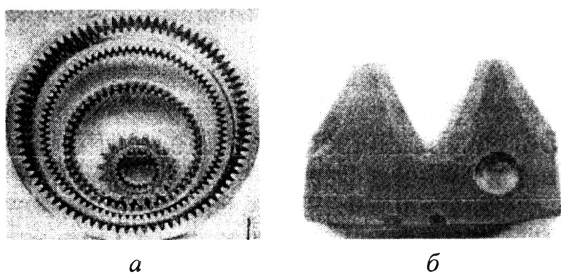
Индукционная закалка зубчатых колес: а — шестерни, подвергаемые поверхностной индукционной закалке; б — зона закалки на зубчатой поверхности шестерни
